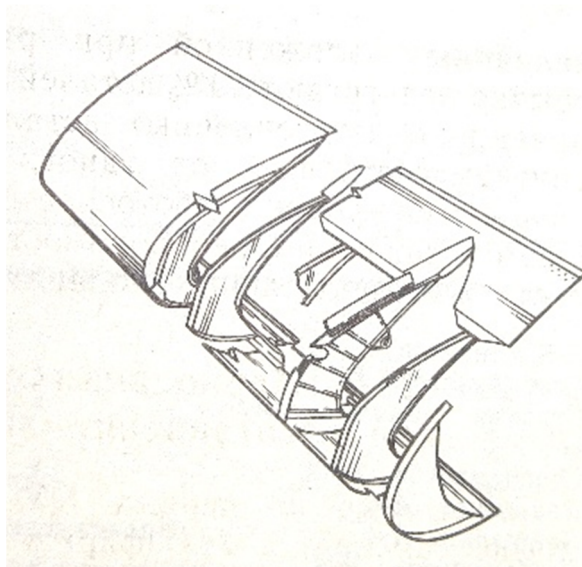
Конструкція передкрилка з боропластика літака С-5А
